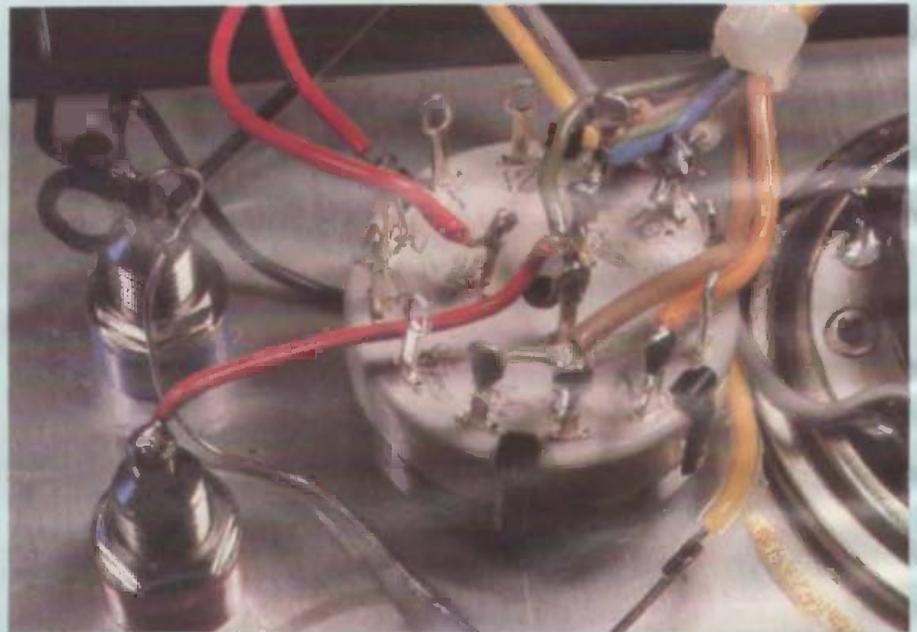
Gros plan sur le câblage du commutateur rotatif.
